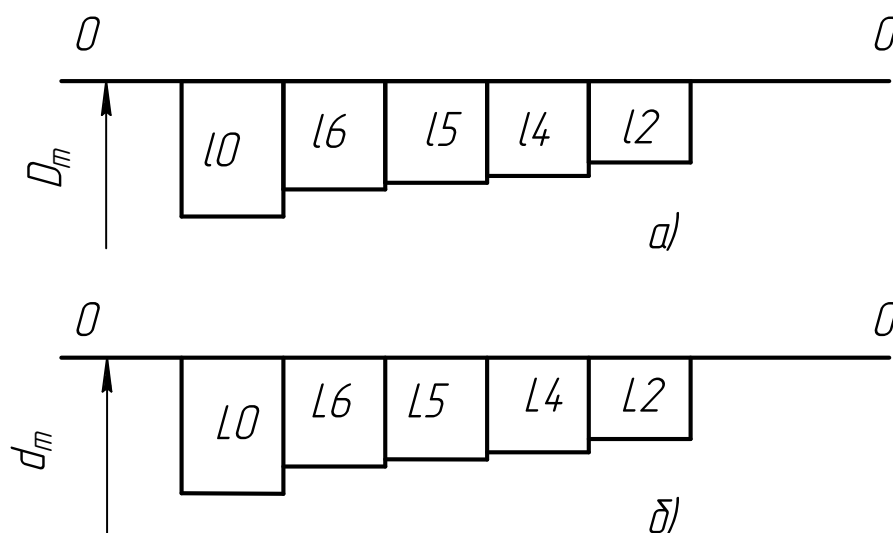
Расположение полей допусков на диаметры колец подшипников качения
